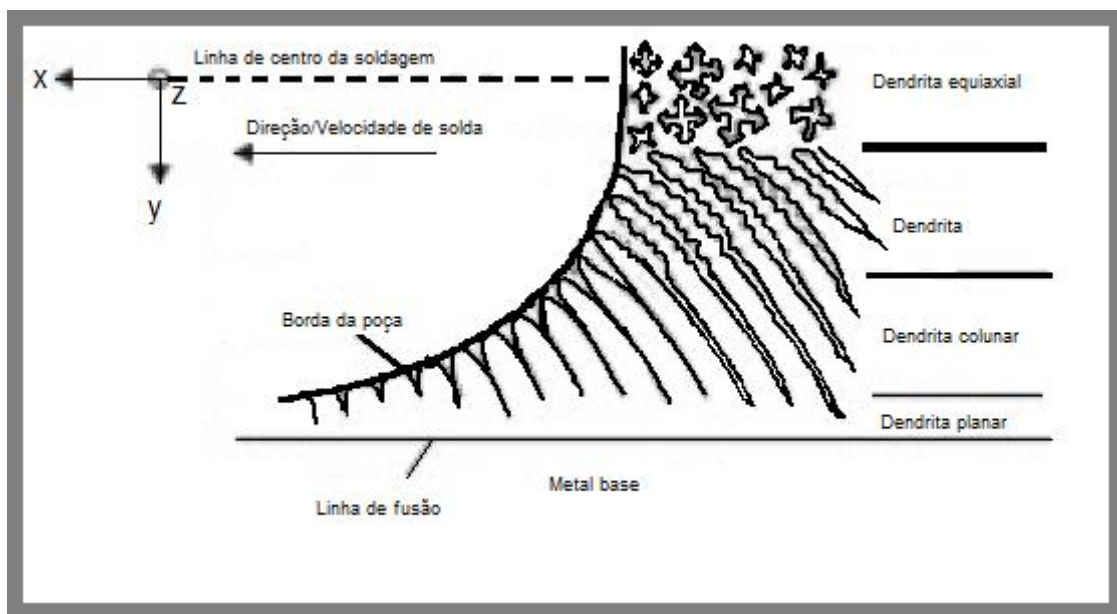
Formação de grãos no processo de soldagem TIG. Fonte: SCHEMP (2014).
